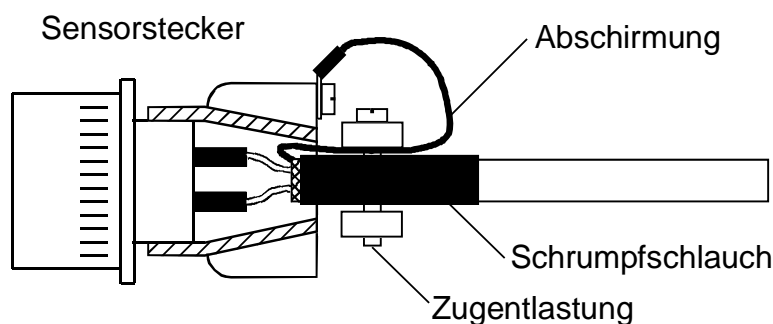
Beispiel einer Schirmbefestigung im Stecker
